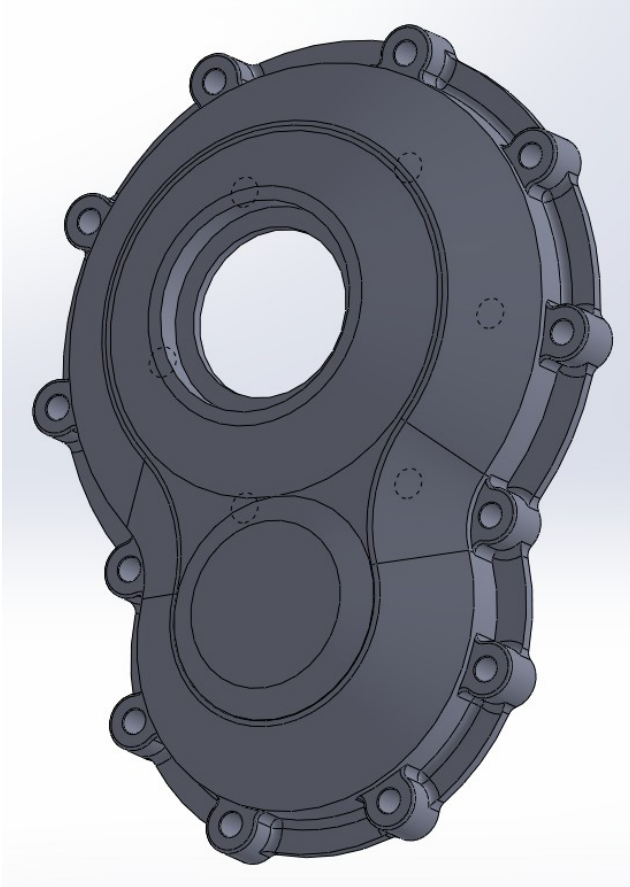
Carter lato elica, vista $\frac{3}{4}$ retro –
